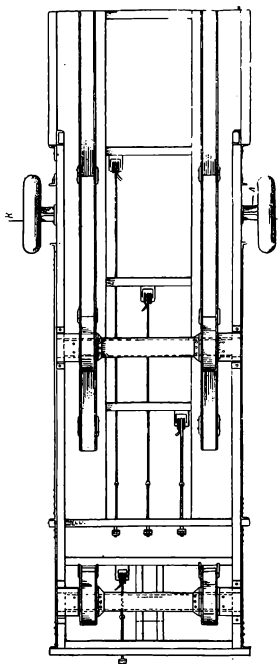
Деталь устройства опор для поддерживания задних колес автомобилей в полуприцепке Мак-Грин.
